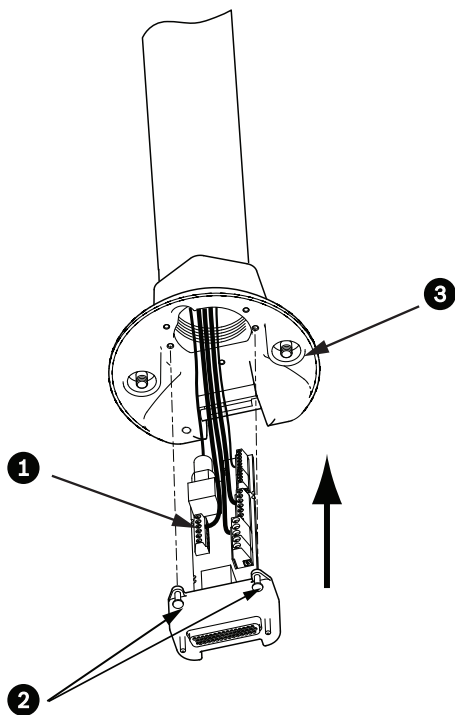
Сборка интерфейсной платы трубы и колпачка камеры
